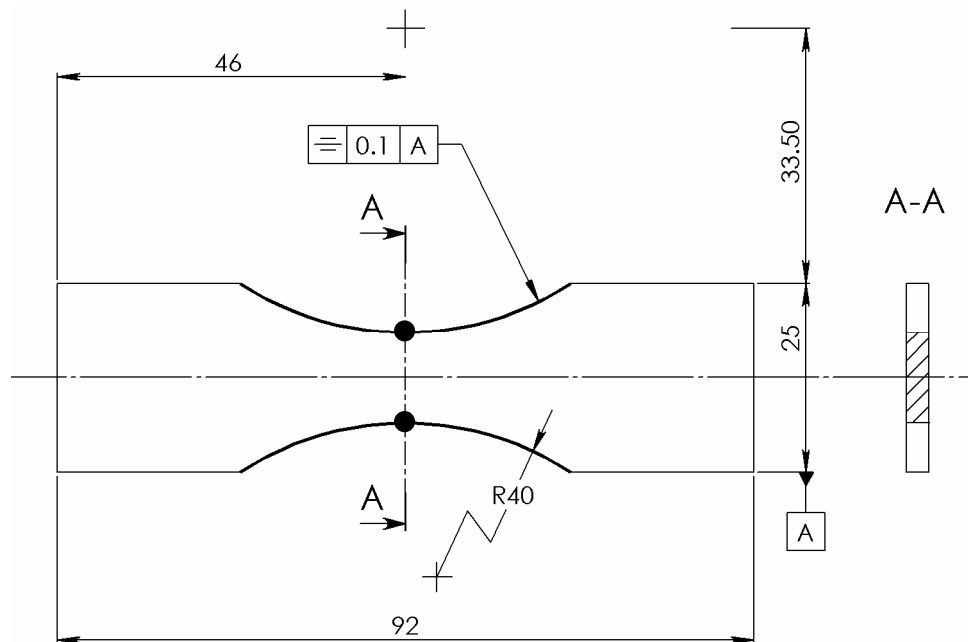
Seconde géométrie d'éprouvette plate de fatigue
